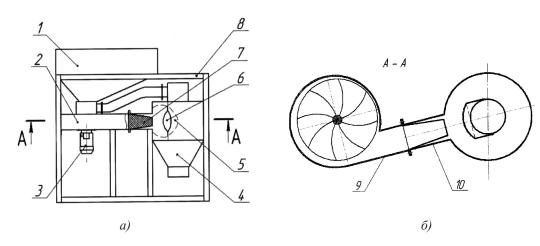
Устройство для снятия плодовых оболочек с зерна: а) — общий вид устройства; б) — разрез А-А; 1 —бункер питающий; 2 — вентилятор; 3 — электродвигатель; 4 — осадитель; 5 — труба вытяжная; 6 — сферическая рабочая пластина; 7 — сетчатый рабочий орган; 8 — рама; 9 — выходной патрубок вентилятора; 10 — входной патрубок осадителя
